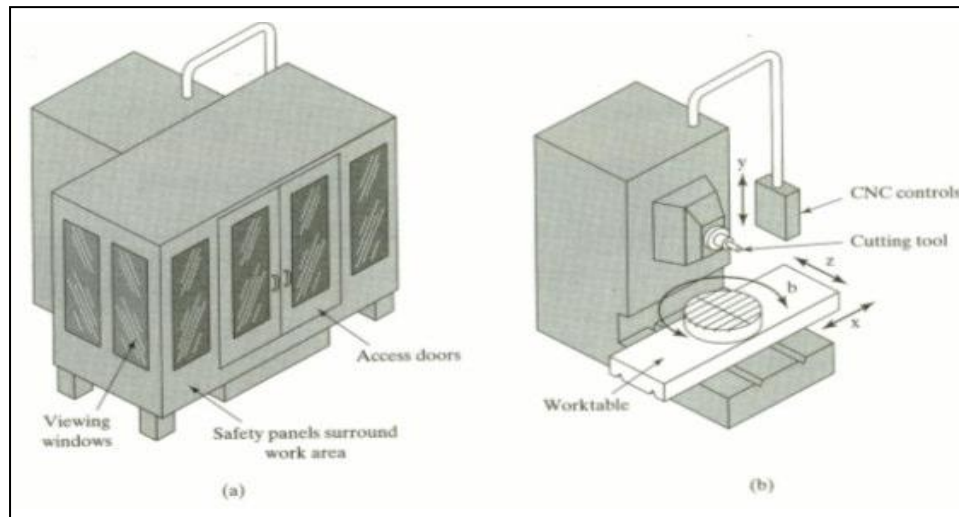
(a) CNC horizontal e (b) CNC sem a proteção (4 eixos) [Groover, 2001].
